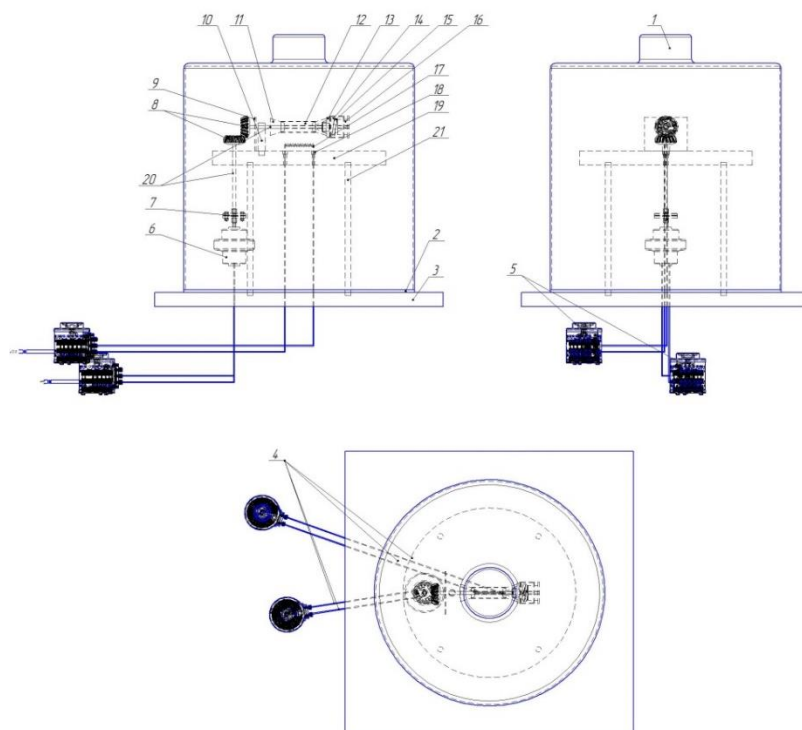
Экспериментальная установка для термовакuumного напыления тонких пленок: 1—купол; 2—силиконовая прокладка; 3—плита; 4—питающие провода; 5—ЛАТР; 6—электродвигатель; 7—муфта соединительная; 8—зубчатые колеса; 9—экран; 10—опора; 11—конус; 12—заготовка; 13—прижим; 14—корпус; 15—прижимная шайба; 16—фиксирующая гайка; 17—металлический испаряющийся материал; 18—фиксирующая гайка; 19—зажим; 20—вал; 21—стойка
